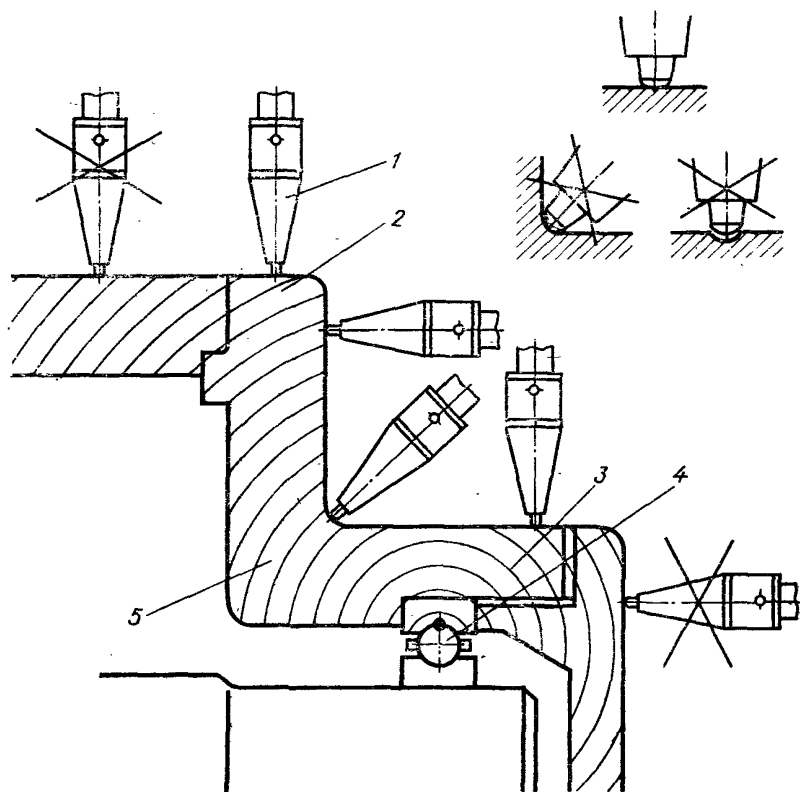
Правила измерения ударных импульсов подшипников качения: 1 — индикаторный щуп прибора ИСП-1; 2 — корпус подшипника; 3 — распространение волны напряжений; 4 — подшипник качения с дефектом; 5 — зона действия ударных импульсов
